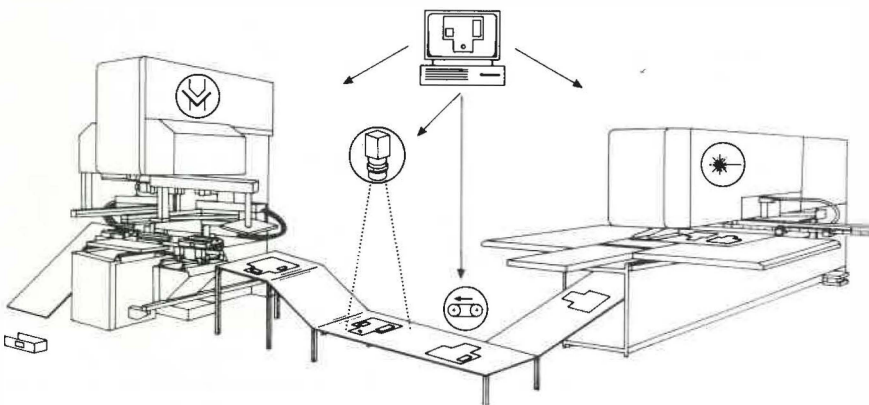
Die Blechteile werden auf einer 2D-Laserstrahlanlage zugeschnitten und anschließend auf einer Biegemaschine fertigbearbeitet
